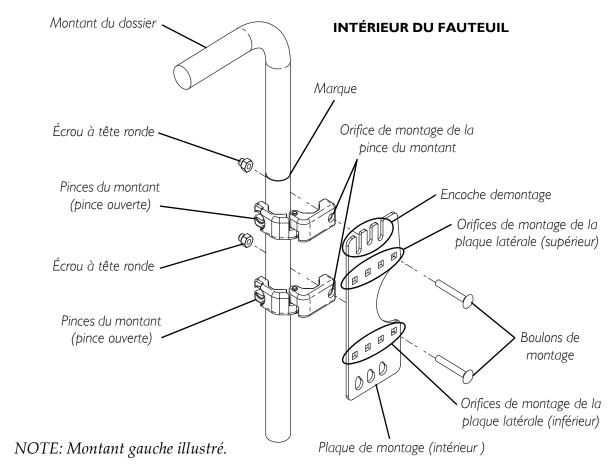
INSTALLER LES PLAQUES LATÉRALES
